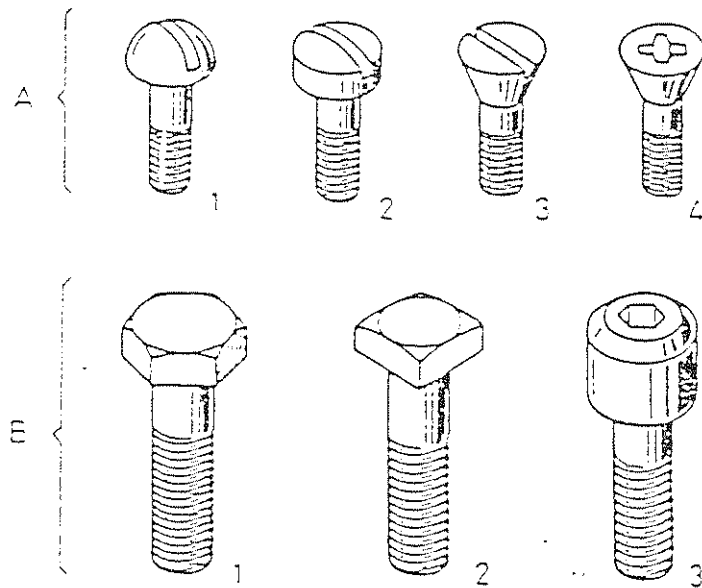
/ 4.- Formas geométricas de las cabezas de los tornillos.
